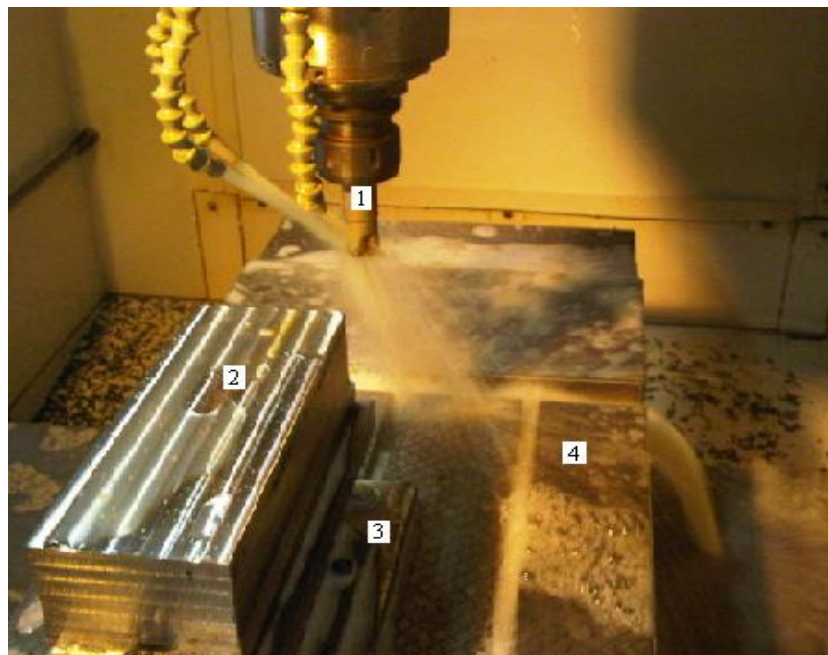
Montagem do corpo de prova: 1) ferramenta; 2) corpo de prova; 3) dispositivo de fixação do corpo de prova; 4) mesa fresadora.
